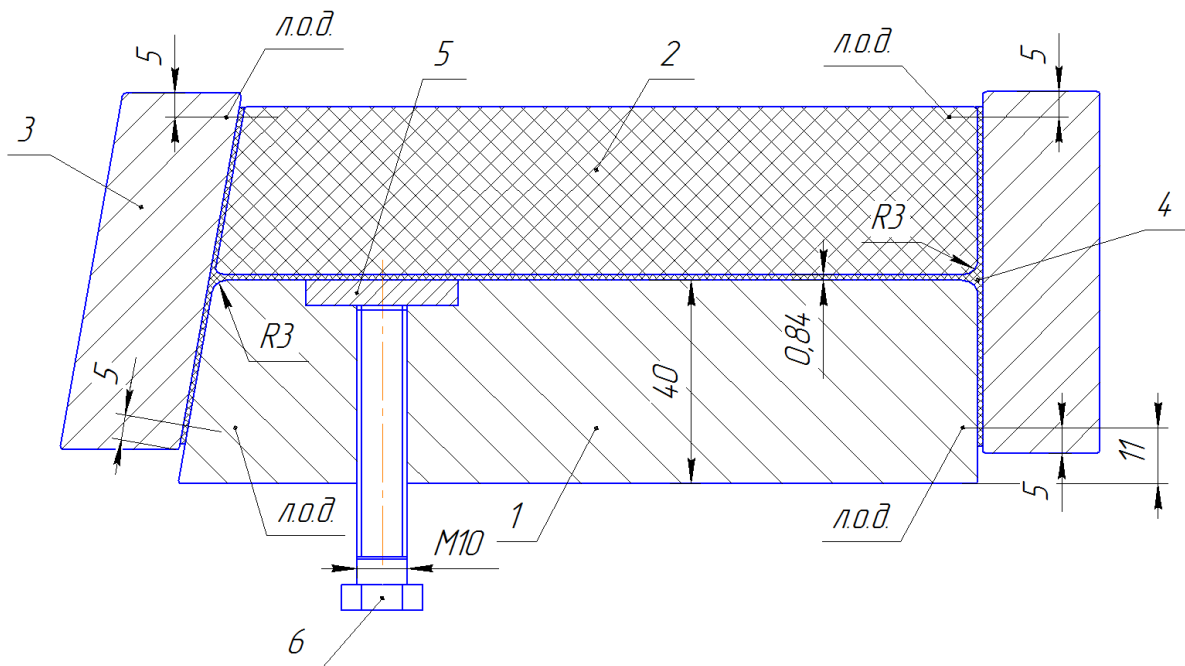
Конструктивні особливості оснащення з використанням формуючих елементів з Aircast 3700 (1 – металічна оправка; 2 – оправка із Aircast 3700; 3 – обойма; 4 – фальшдеталь; 5 – вставка 6 – болт).
